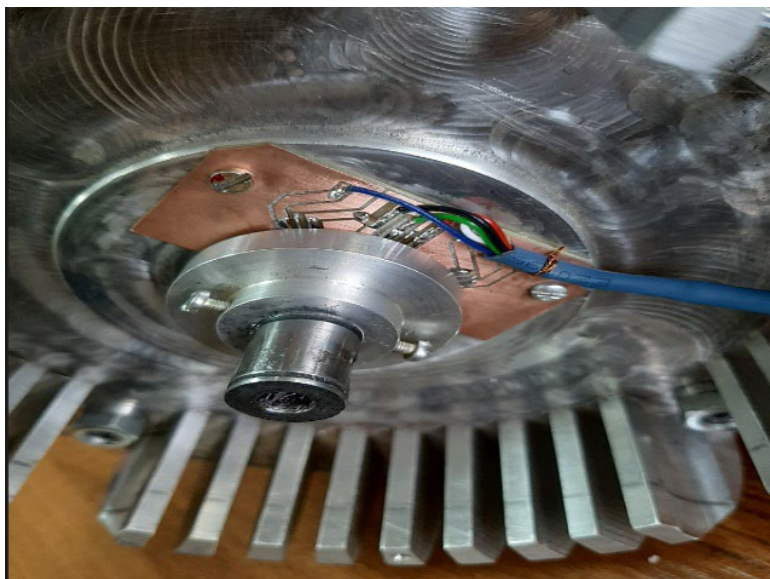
Фрагмент монтажа датчиков Холла на корпусе двигателя (опытный образец)
